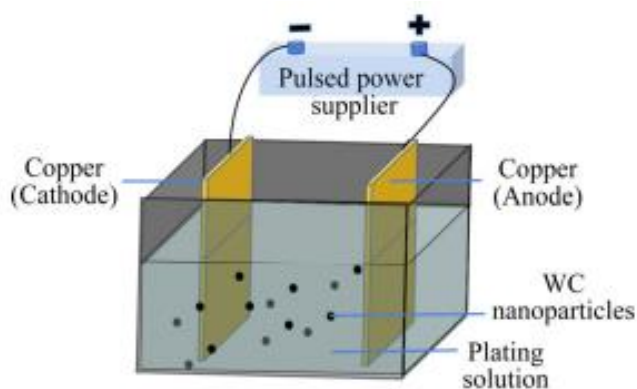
Základní technologický postup galvanického pokovování [37]
